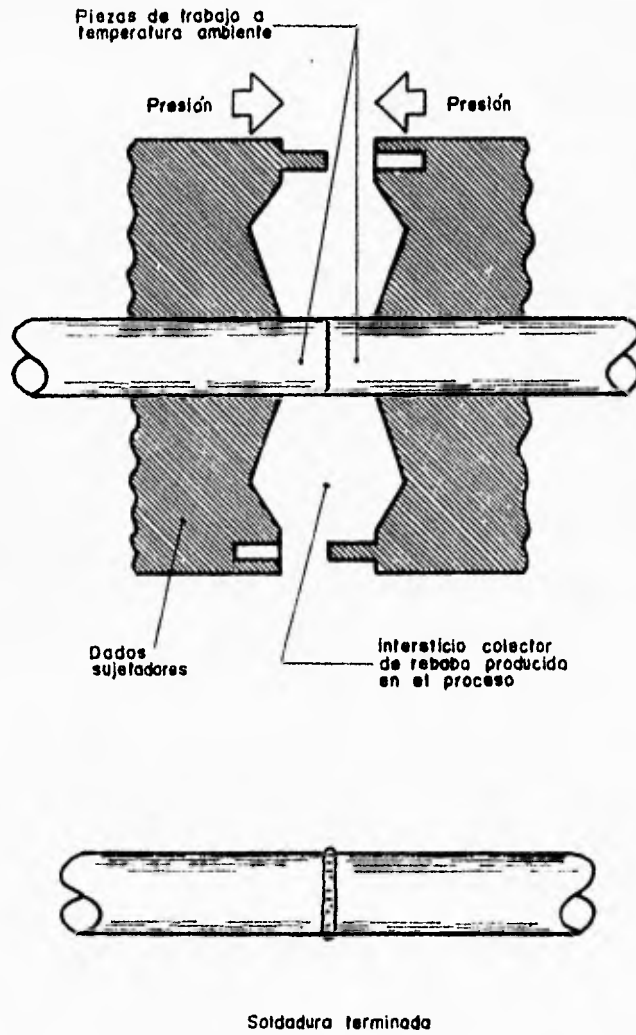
I. Soldadura en frío (CW)
